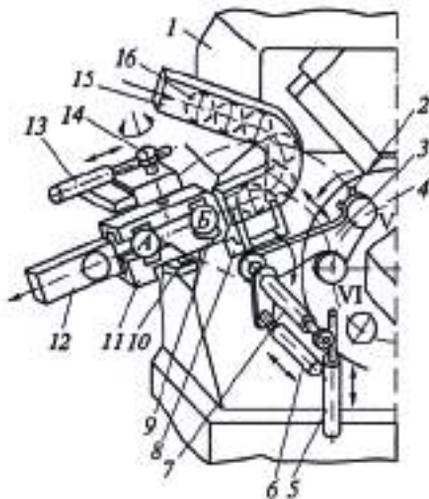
Загрузочное устройство, встроенное в горизонтальный многошпиндельный станок-автомат: 1 – станок; 2 – захват; 3 – рука; 4 – шпиндельный блок; 5, 6, 13 – гидроцилиндры; 7, 10 – оси; 8 – отсекатель; 9 – собачка; 11 – кантователь; 12 – отводящий лоток; 14 – реечная передача; 15 – подводный лоток; 16 – заготовка; А, Б – полости кантователя; V, VI – позиции патронов
